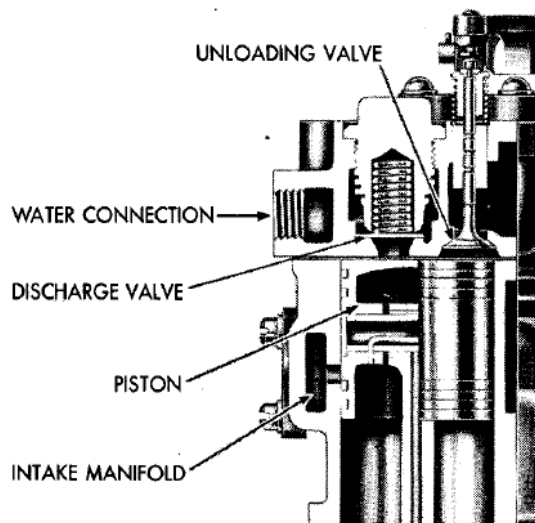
Corte transversal del cilindro y detalle de la cámara de compresión.
